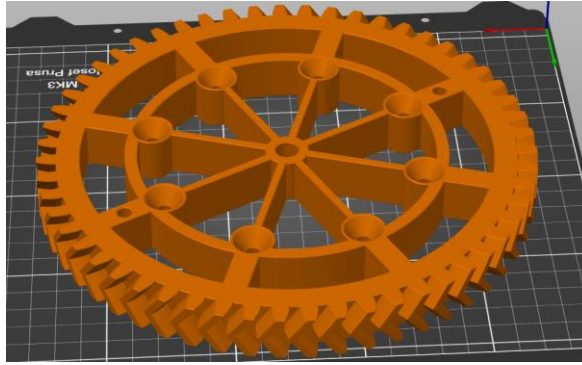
Engranaje del carrete de filamento lado izquierdo-derecho.
